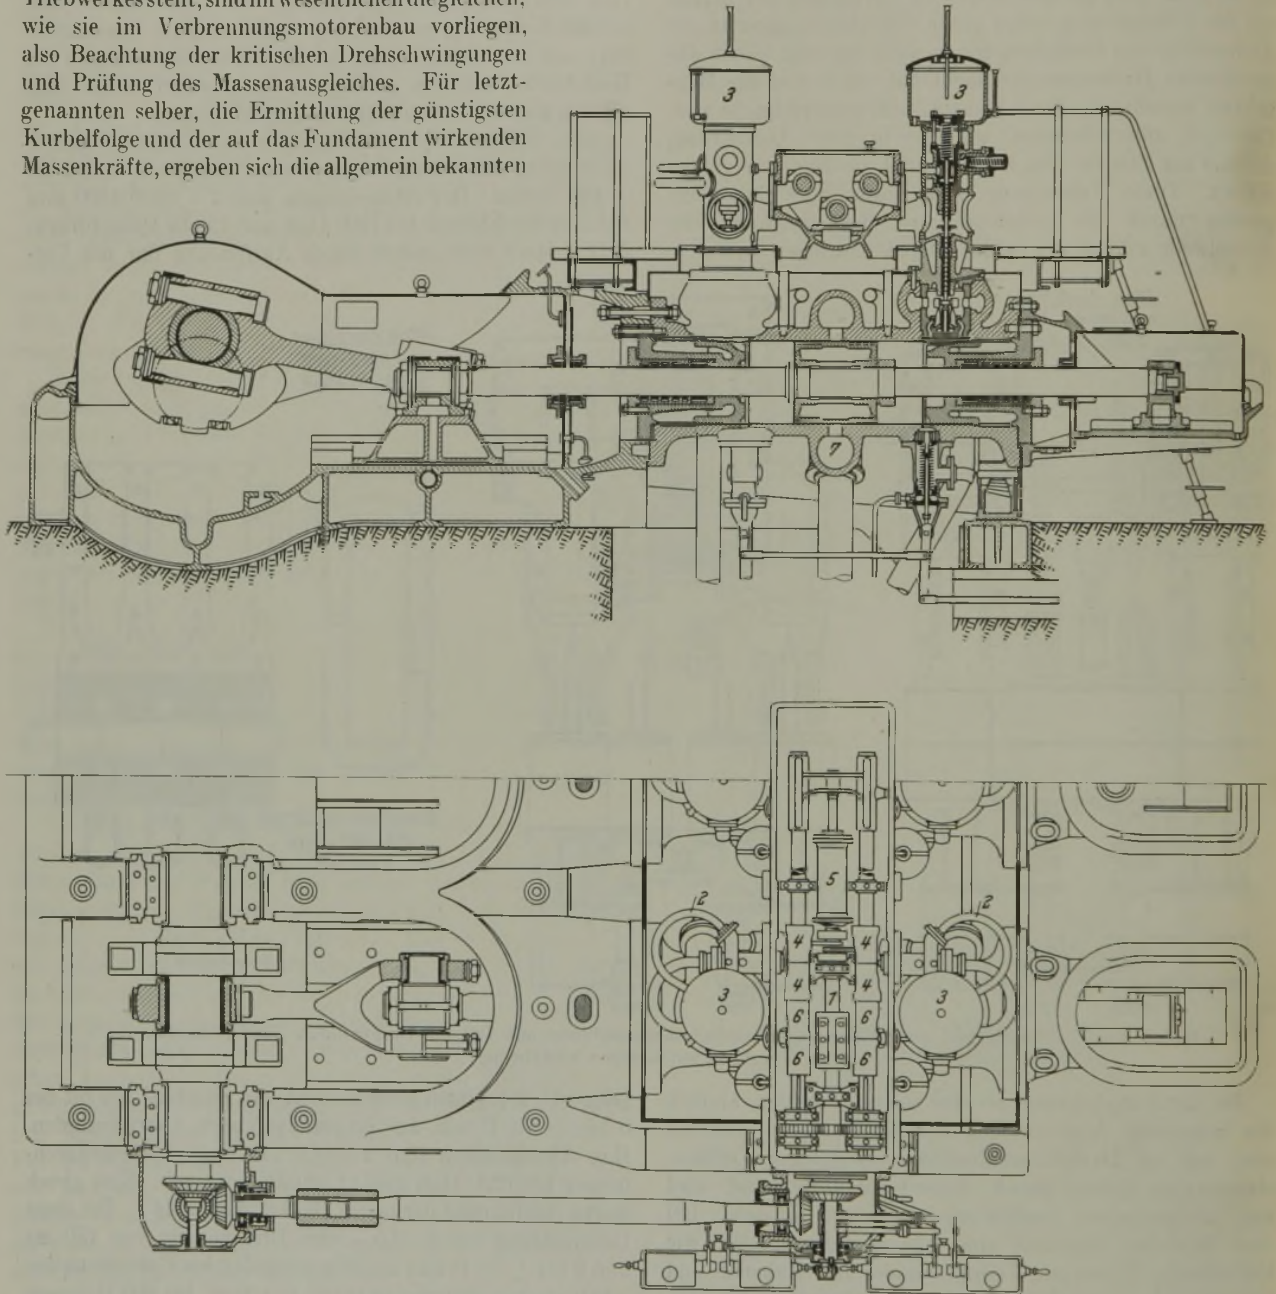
Umkehrdampfmaschine mit ölhdraulischer Steuerung.
